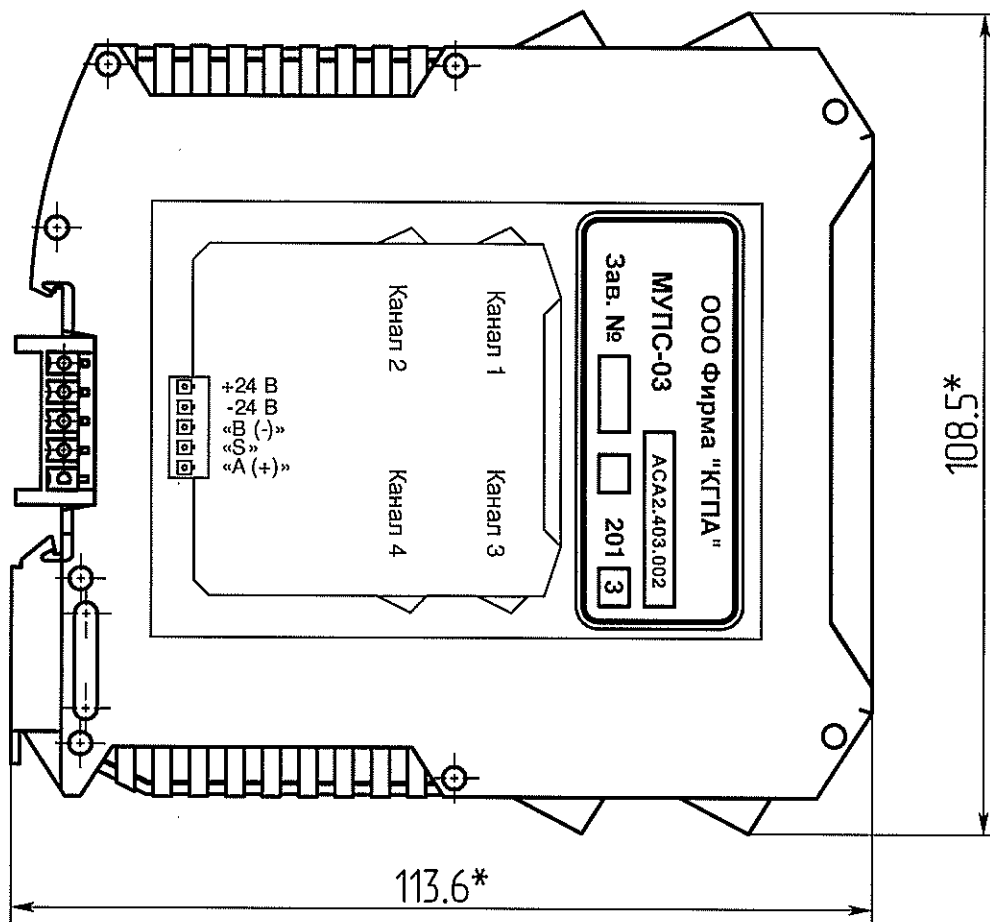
Внешний вид модуля МУПС-03 с шинным соединителем (вид сбоку)
